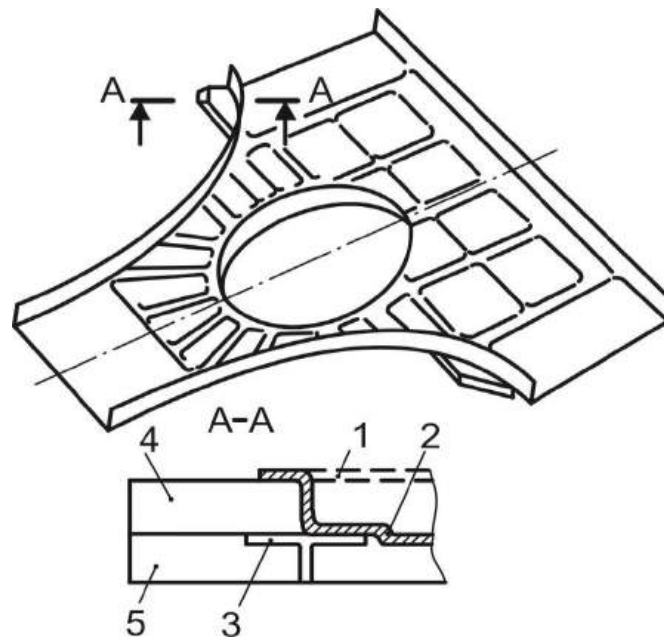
Схема застосування надпластичного формування і дифузійного зварювання: 1 – листова заготовка; 2 – відформована діафрагма; 3 – попередньо встановлені деталі; 4 – матриця; 5 – вставка
